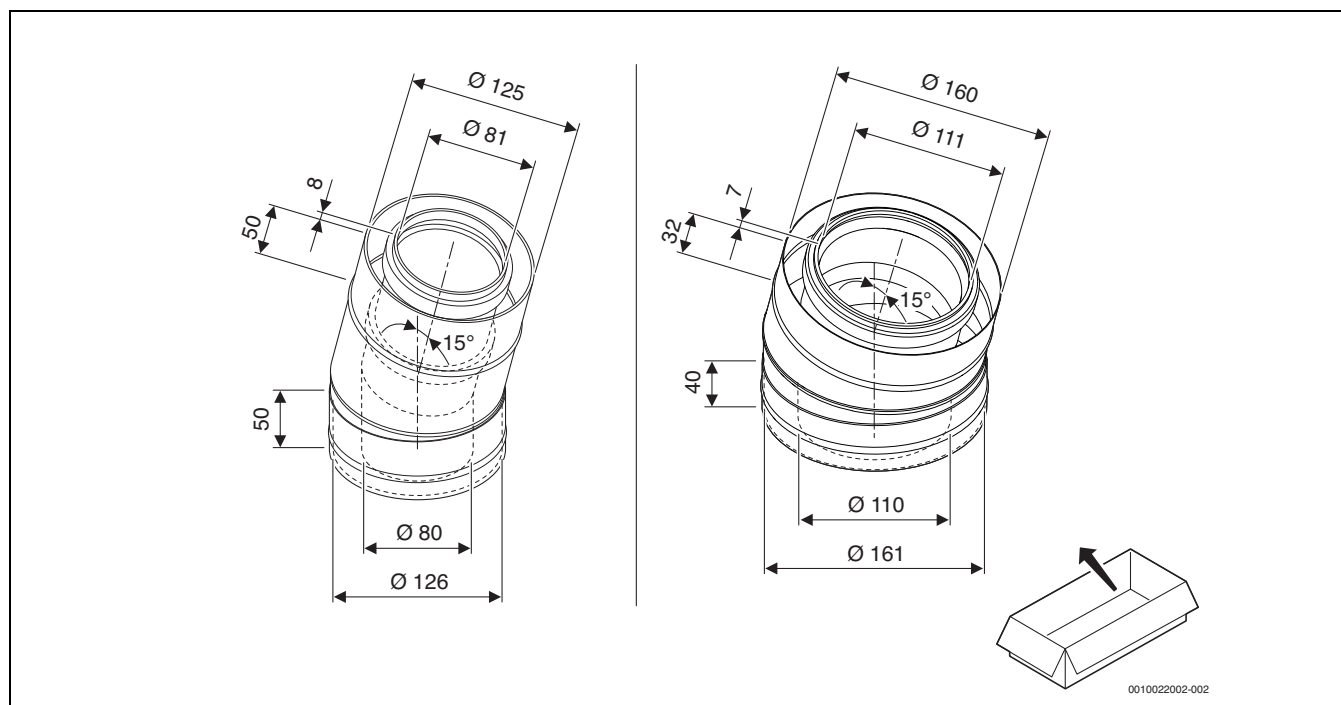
Ø 80/125 mm: 7738112703, Ø 110/160 mm: 7738113143
